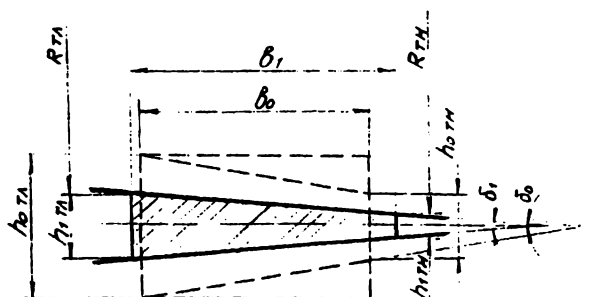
Схема прокатки клиновидного профиля из клиновидной или прямоугольной заготовки
